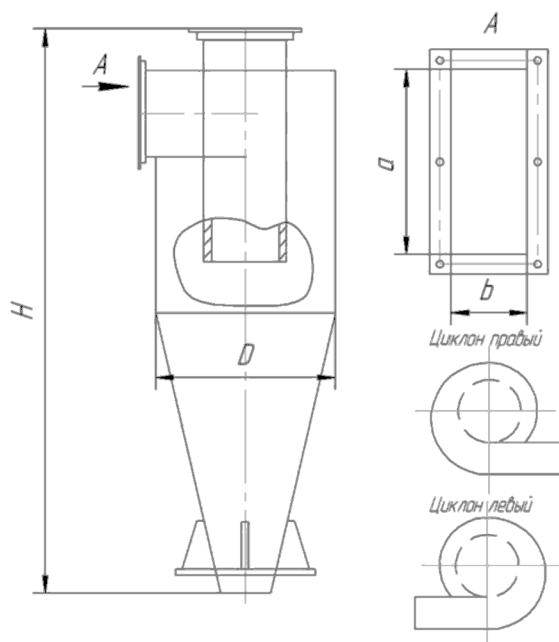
Габаритные и присоединительные размеры циклонов СЦН-40.
